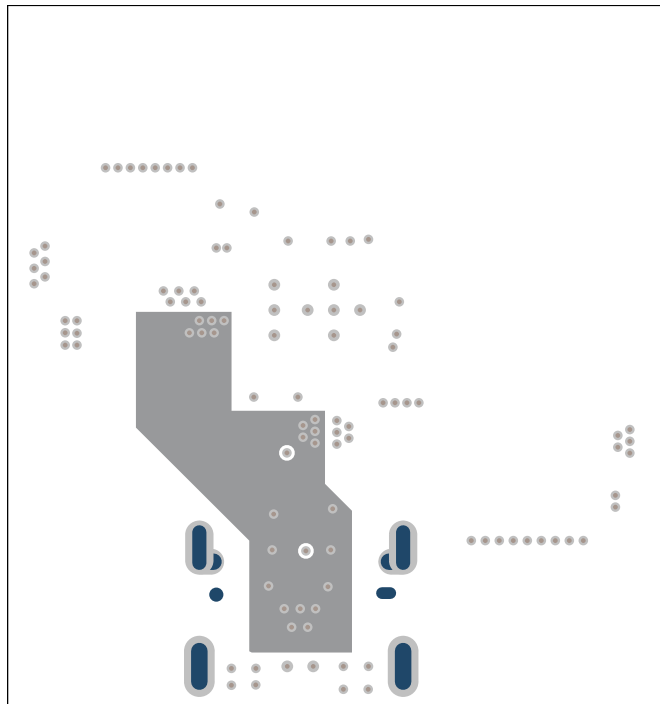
TPS25751D PCB Layout - Internal Power Layer
